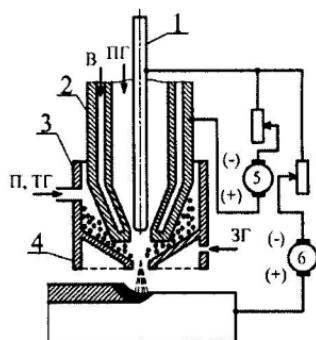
Схема плазмово-порошкового наплавлення
